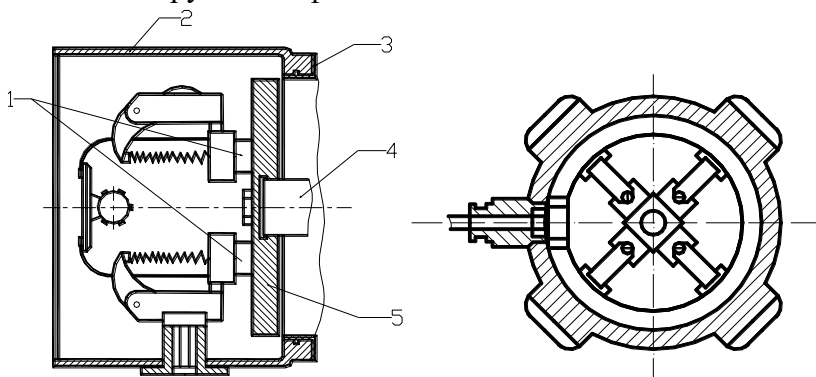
Токоподвод к шпинделю шлифовального станка (аксиальное исполнение): 1 - корпус; 2 - щетки; 3 - щеткодержатели; 4 - шпиндель; 5 - токосъемный торец
